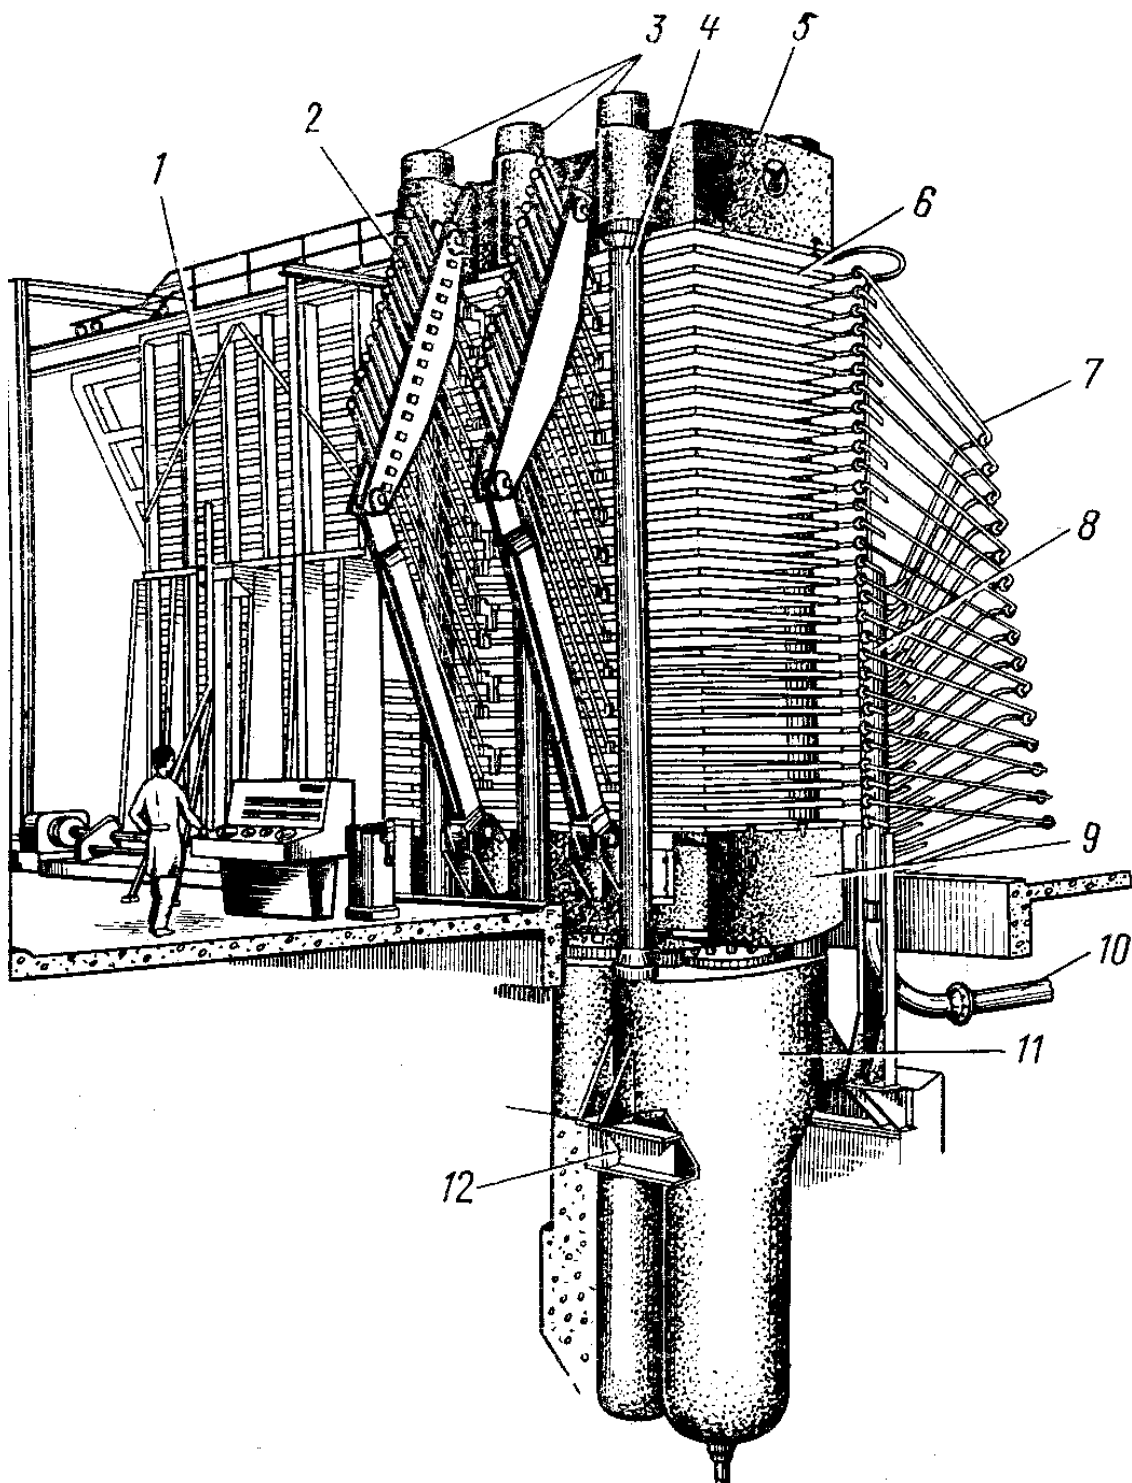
Гидравлический 29-этажный пресс колонной конструкции:
